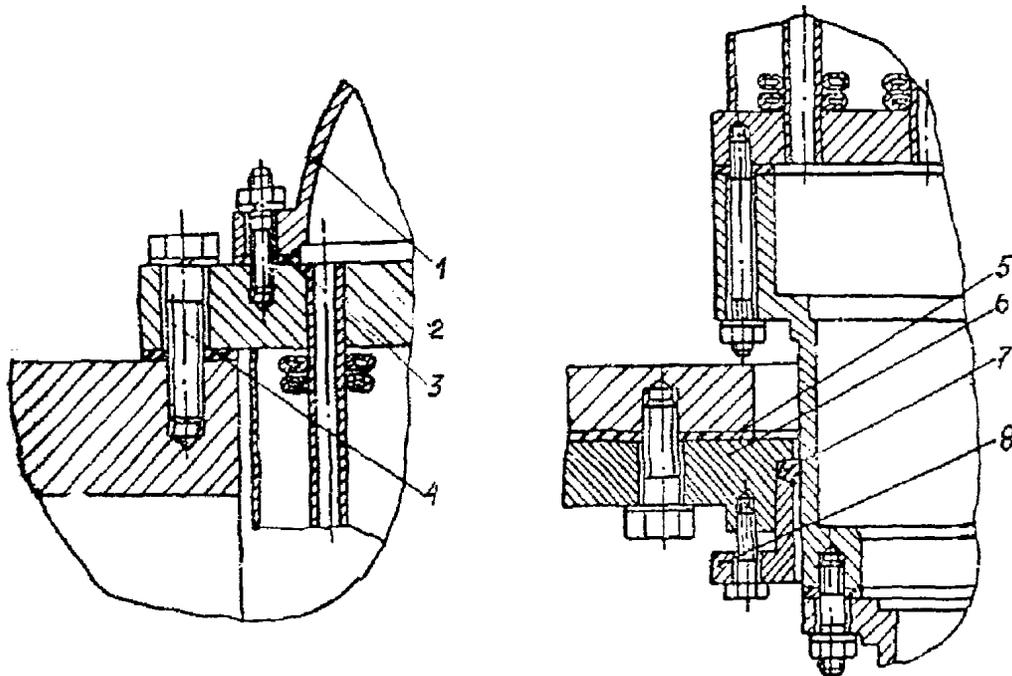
Установка газоохладителя в корпусе турбогенератора:
